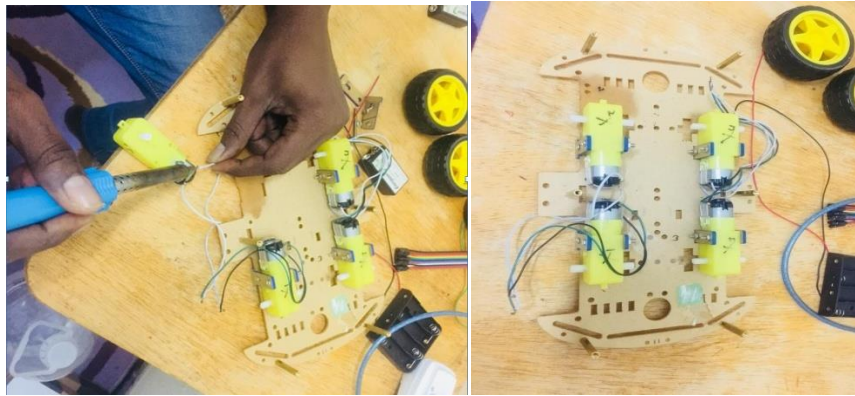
Soudage du fil des moteurs et les placer sur la partie inférieure du châssis
